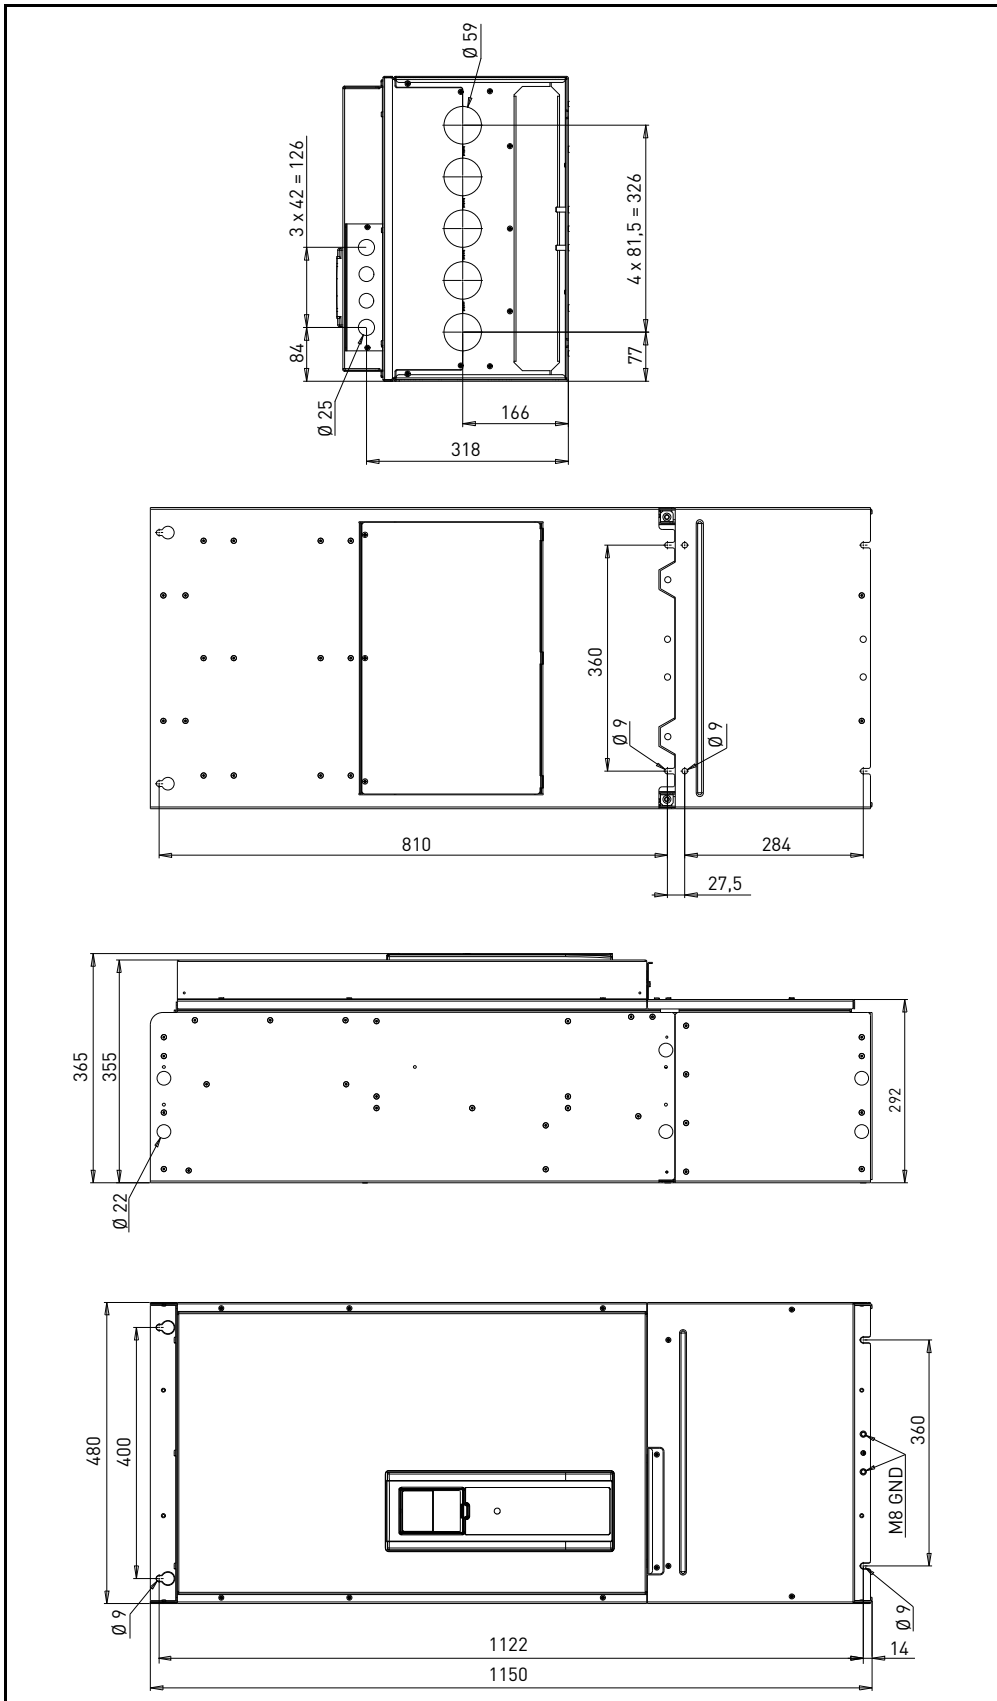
Dimensões do inversor de CA Vacon, MR9 IP21 e IP54
